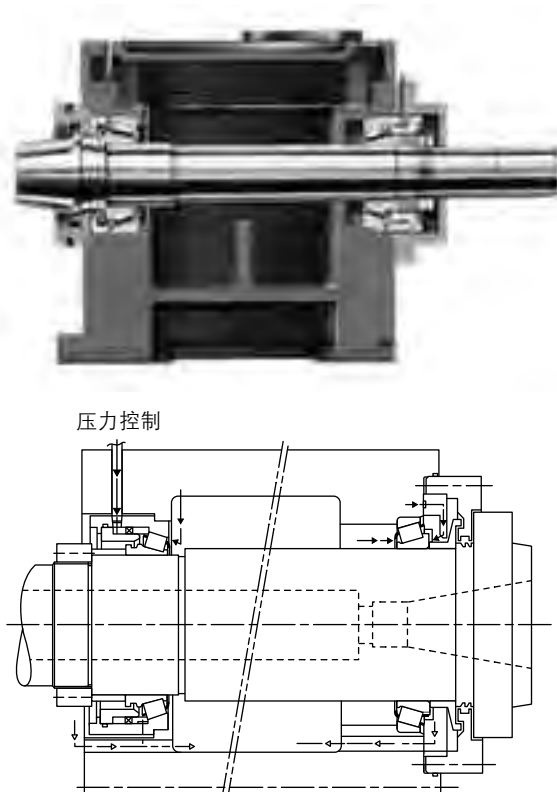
采用 Hydra-Rib 轴承（有轴向进油冷却）和TSMA 轴承（在滚子两端都有喷油孔用于进油和冷却）的简易安装
